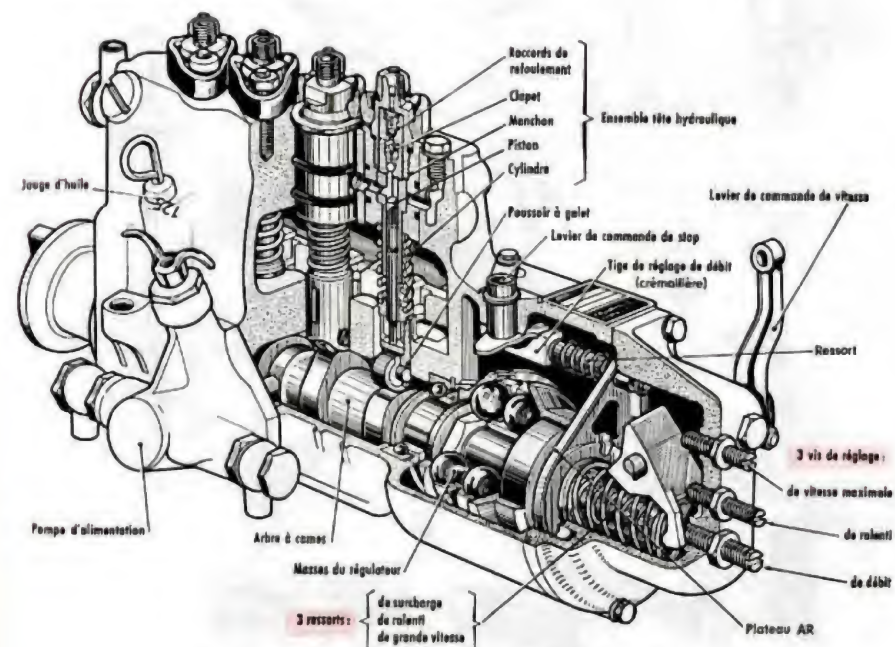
Pompe d'injection monobloc S.I.G.M.A. type C.M.S.
